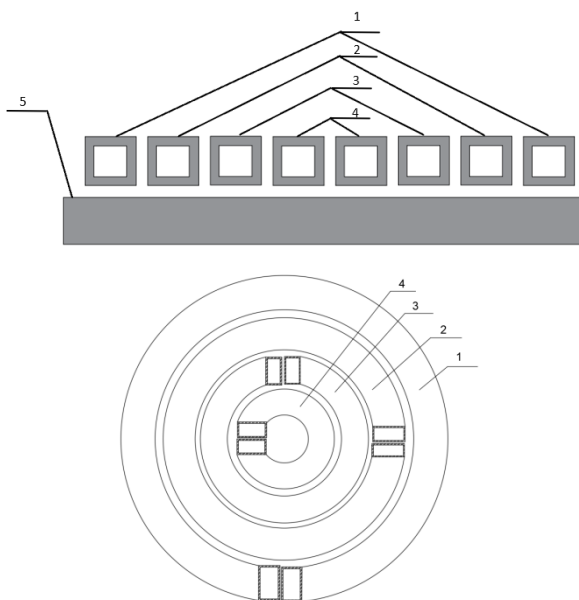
Система индукторов для сквозного нагрева заготовок дискообразной формы
